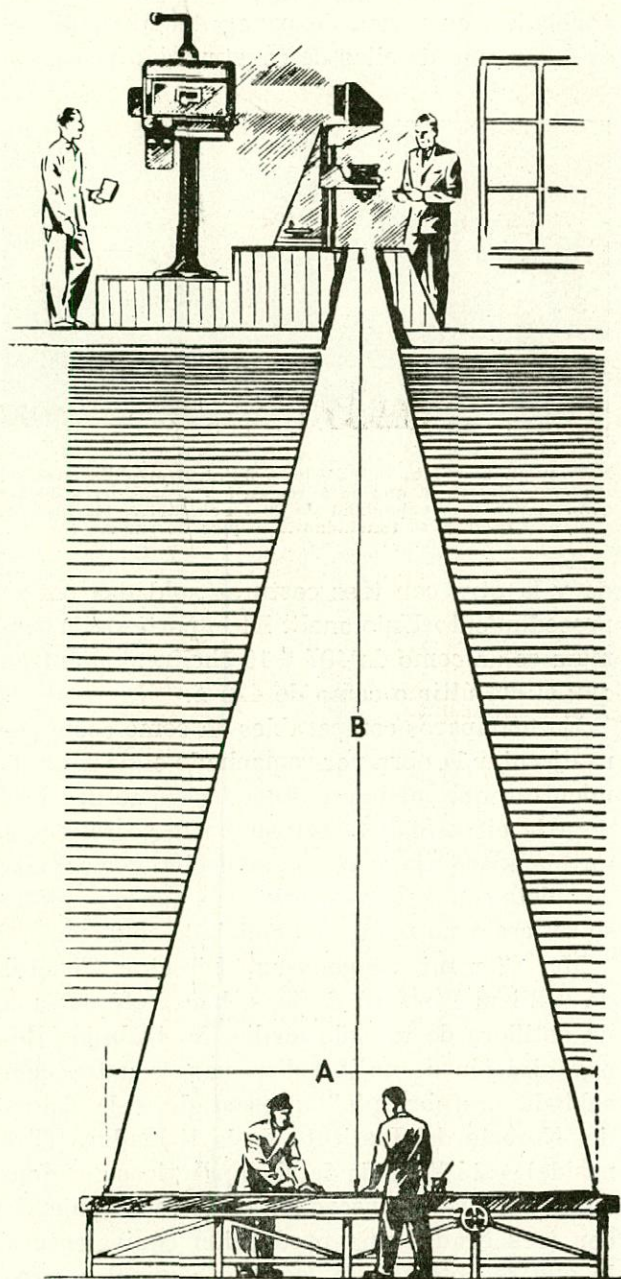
Esquema del aparato de proyección para el marcado de planchas y perfiles.
